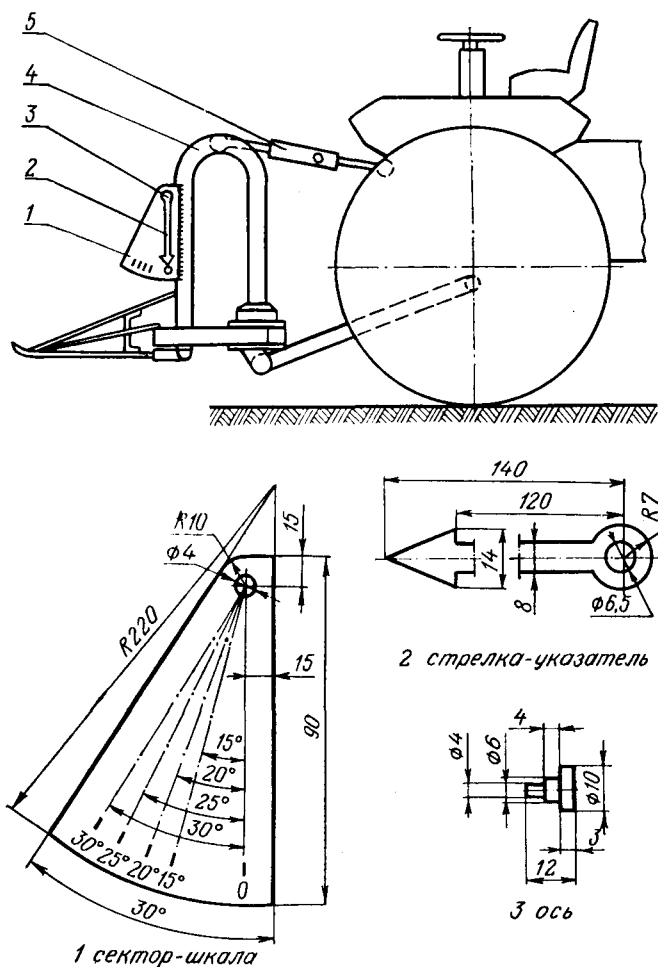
Устройство и крепление приспособления для регулировки наклона льнотеребилки:
